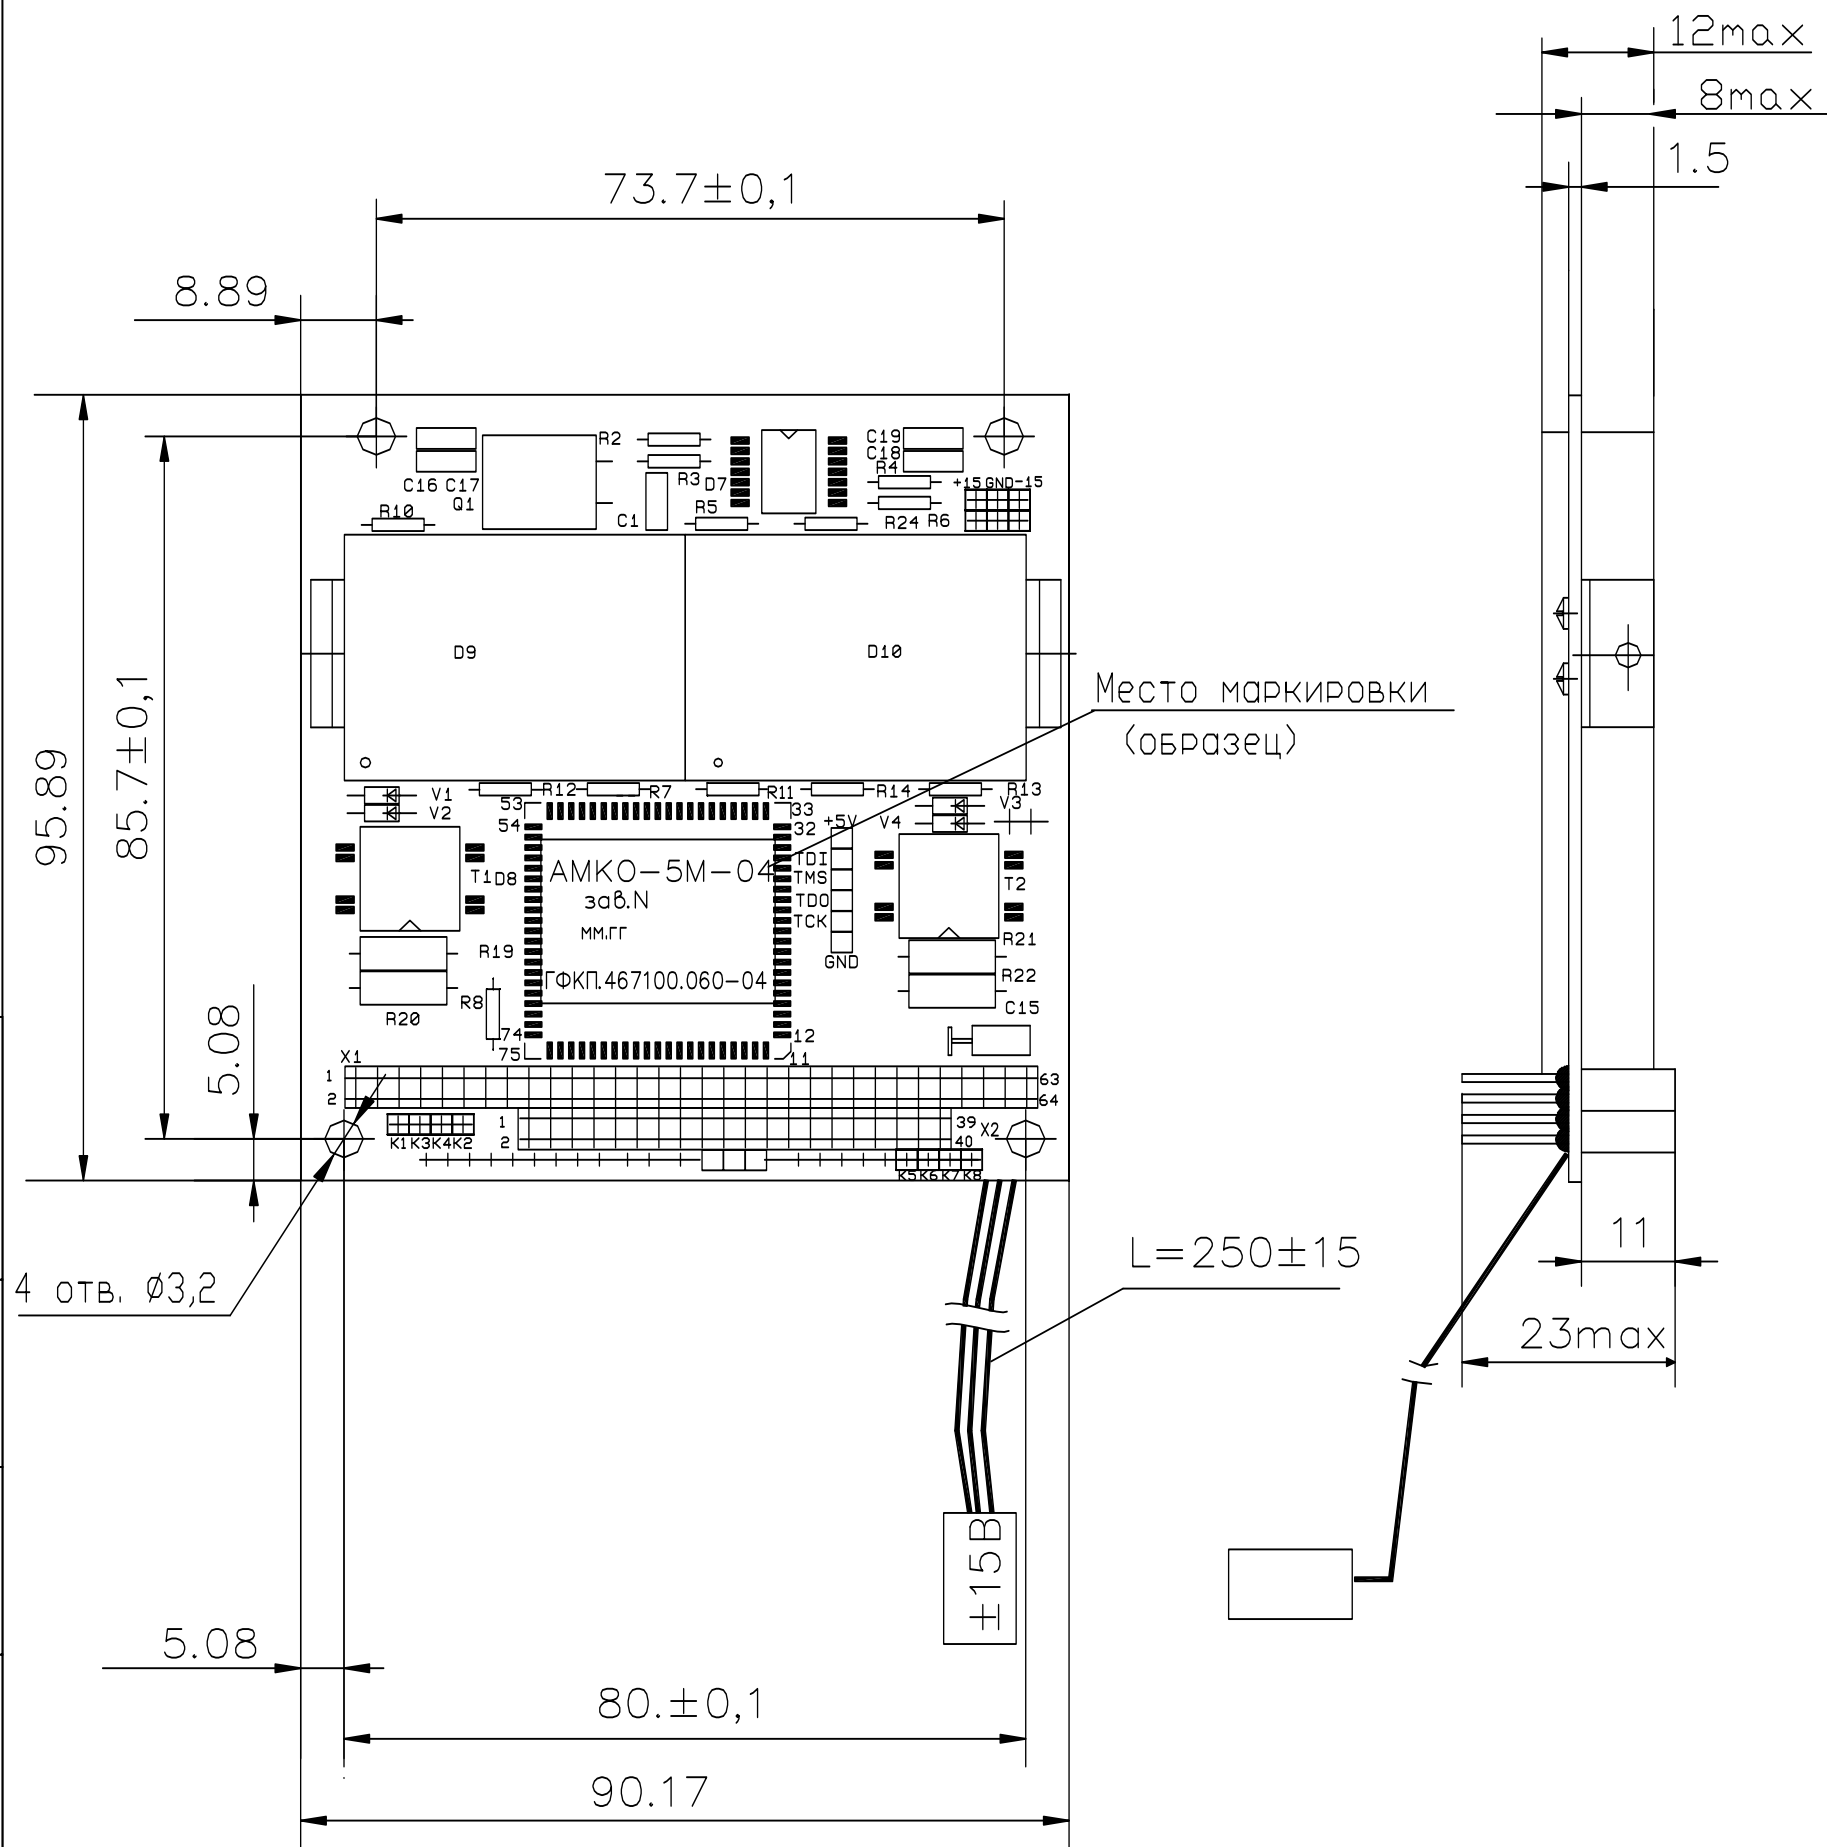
Габаритный чертеж исполнения АМКО-5М-04
